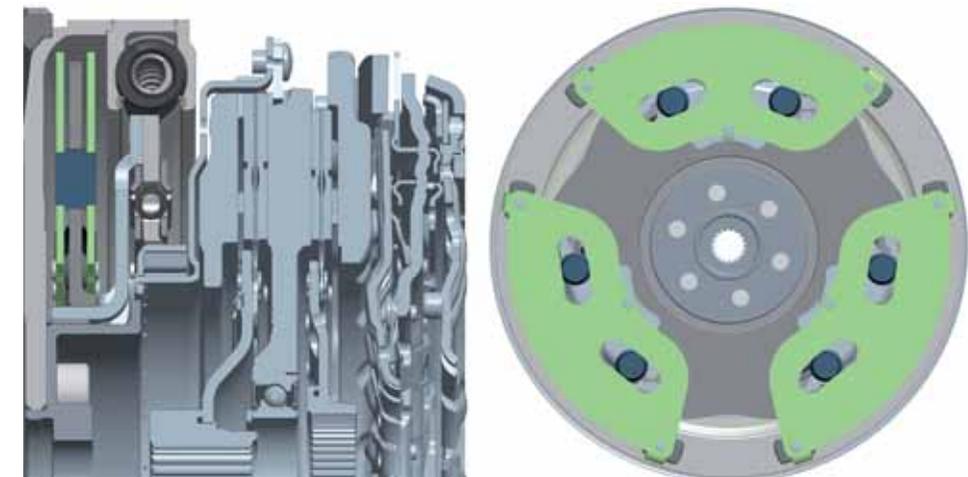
Konstruktion des ZMS mit Fliehkraftpendel für die 0,75te Ordnung für die rollierende Zylinderabschaltung RCD 1.5 des Dreizylindermotors
